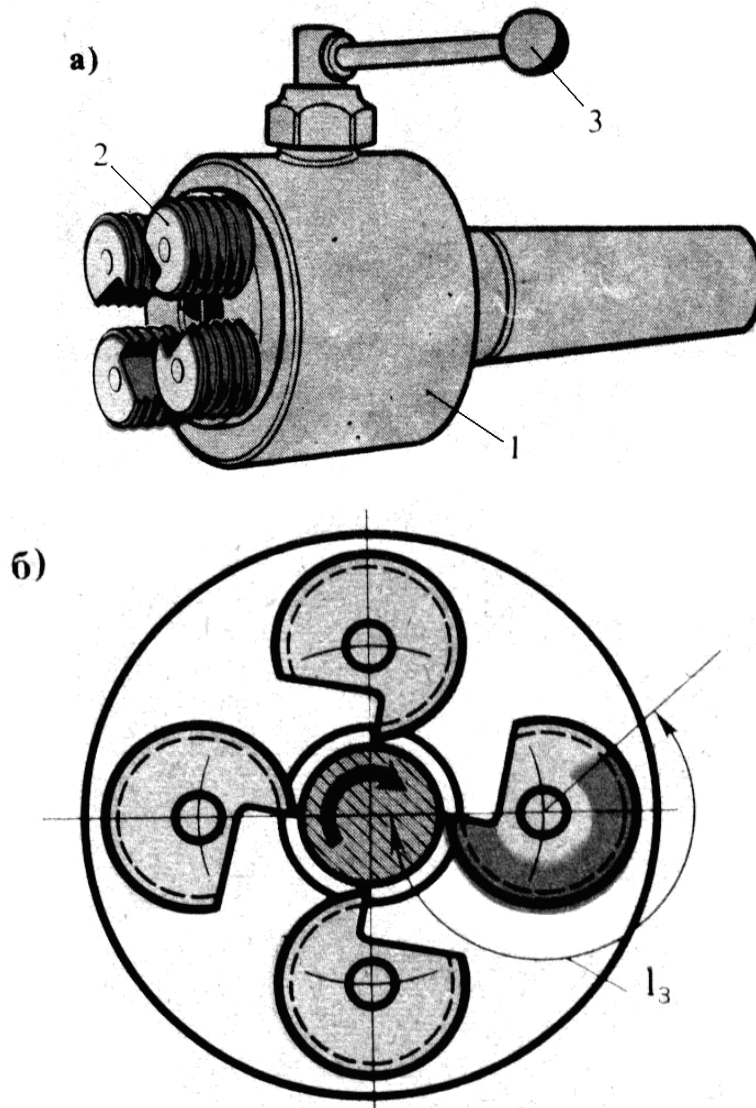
Різенарізна головка: а — загальний вигляд, б — схема роботи гребінок: 1 — корпус, 2 — дискова гребінка, 3 — рукоятка механізму розкриття головки,  $l_3$  — зона заточки гребінки
